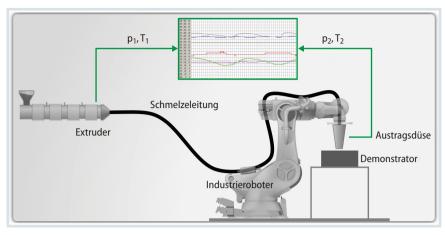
Der Extruder ist mit einer flexiblen Schmelzeleitung mit dem am Industrieroboter befestigten Druckkopf gekoppelt © Fraunhofer IWU
